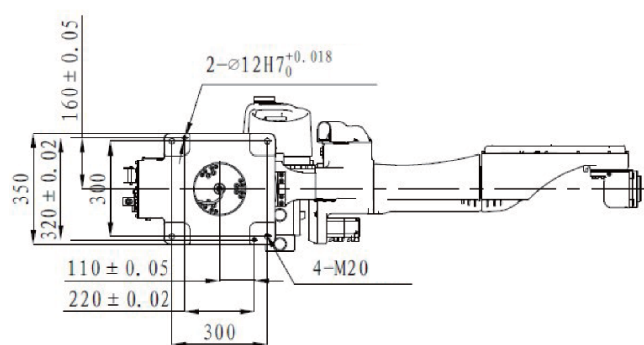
Габаритные чертежи сварочного робота SA6-1440.
